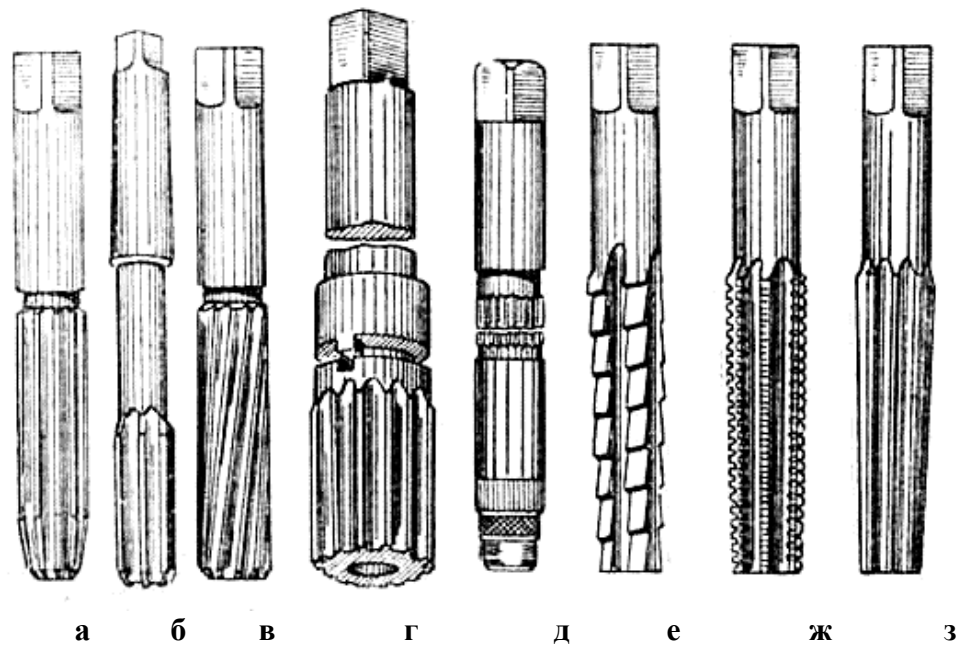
Основні типи разверток: а – з прямими зубами і кінцевою прямою цапфою, б – циліндрична розвертка з прямими зубами, в – циліндрична розвертка з гвинтовими зубами, г – насадна розвертка, д – ступінчаста розвертка, е, ж, з – комплект розверток під кінчну різьбу, відповідно чорнова, проміжна та чистова розвертка
